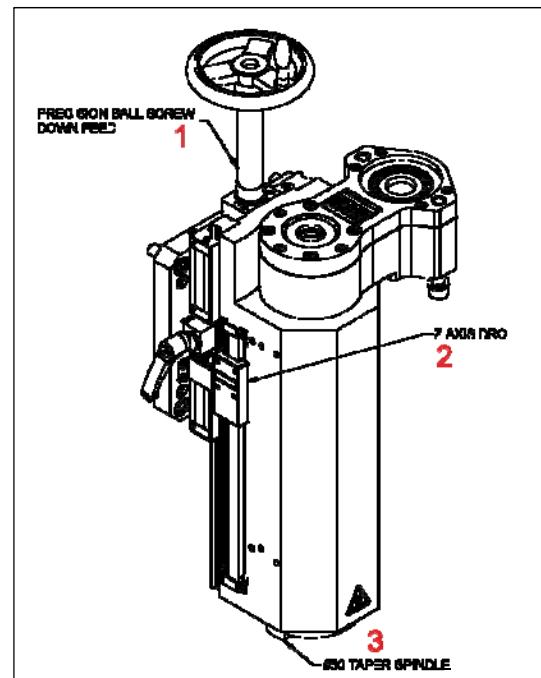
Компоненты фрезерной головки (кат. № 72277)
